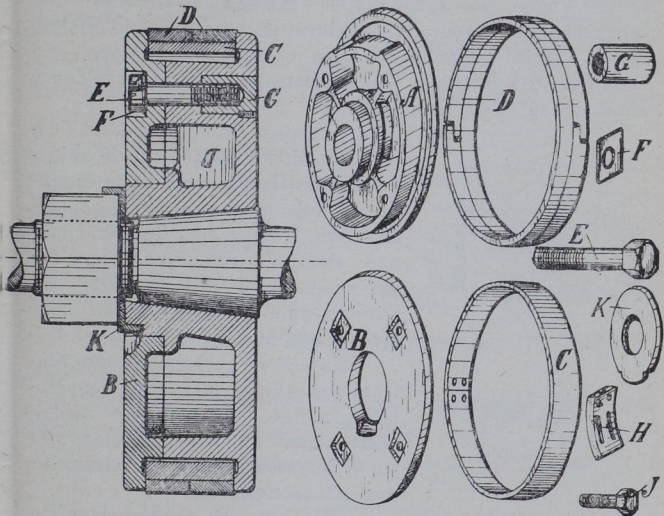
139. Dampfkolben für Maschinen über 400 Cylinderdurchmesser.
